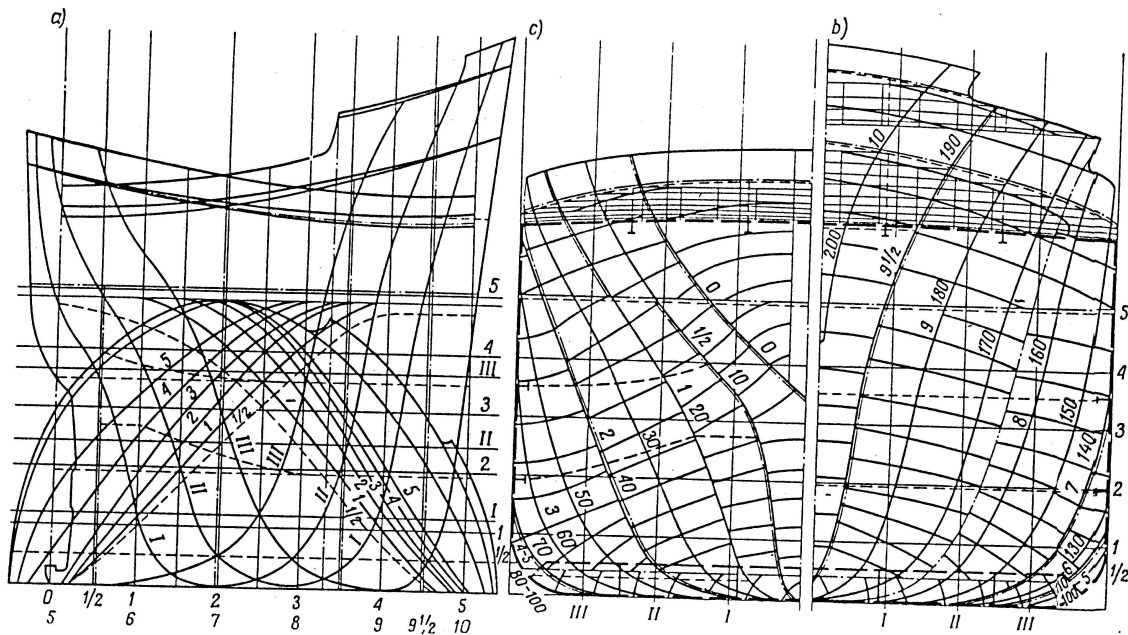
Plano Vertical e sobreposição do plano longitudinal
